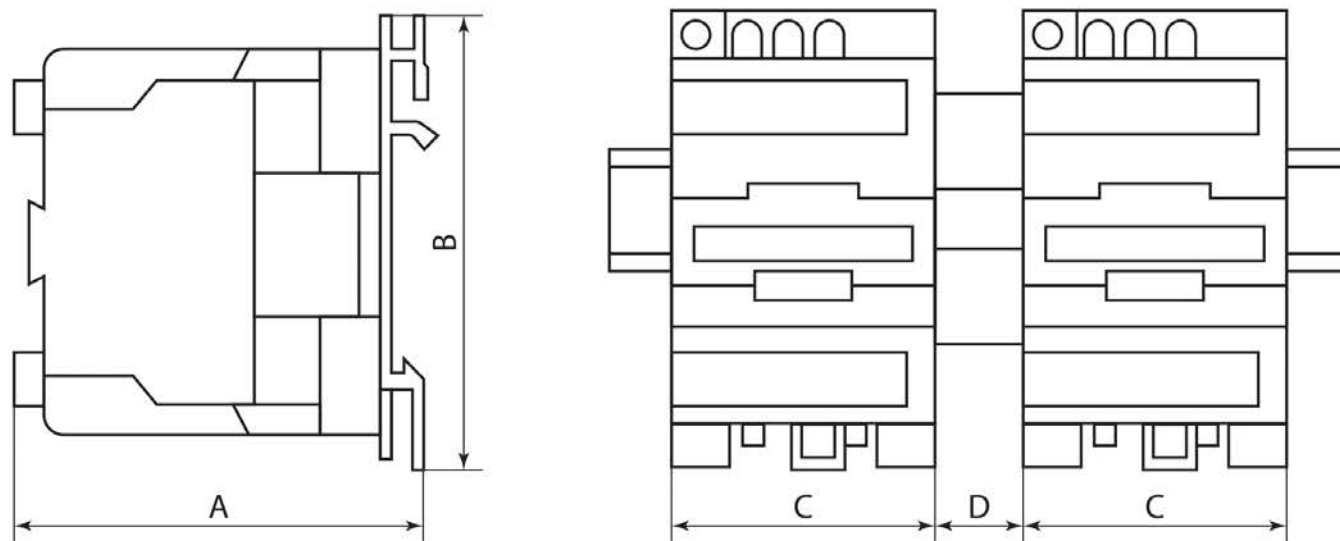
Габаритные размеры реверсивных малогабаритных контакторов 9-25 А
